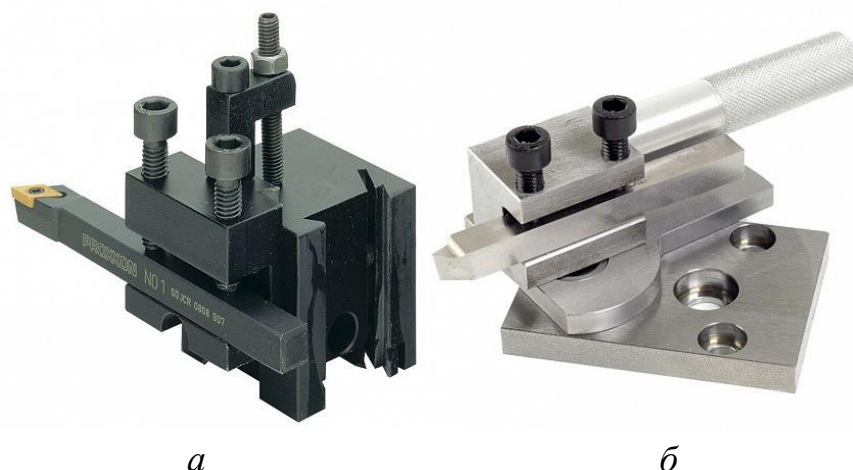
Різцетримачі: а – нерухомий, б – поворотний
